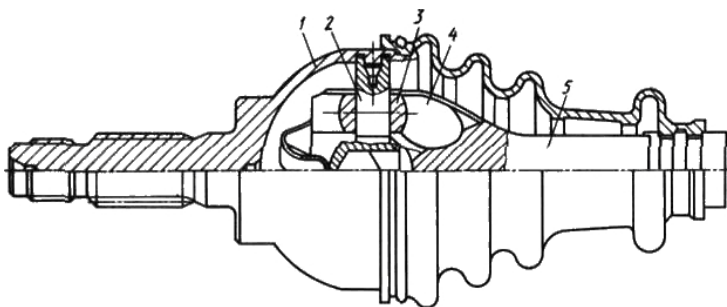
Трехшиповой жесткий карданный шарнир типа «Трипод»: 1 – корпус; 2 – шипы; 3 – ролики; 4 – вилка; 5 – вал
